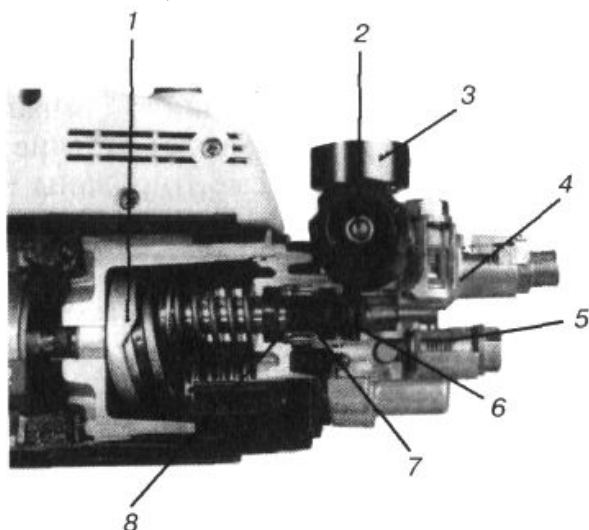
Насос высокого давления: 1 — привод; 2 — регулятор давления; 3 — манометр; 4 — головка насоса; 5 — клапаны; 6 — возвратный клапан; 7 — защитное покрытие от сухого включения и избыточного давления; 8 — трехосевой плунжерный насос
